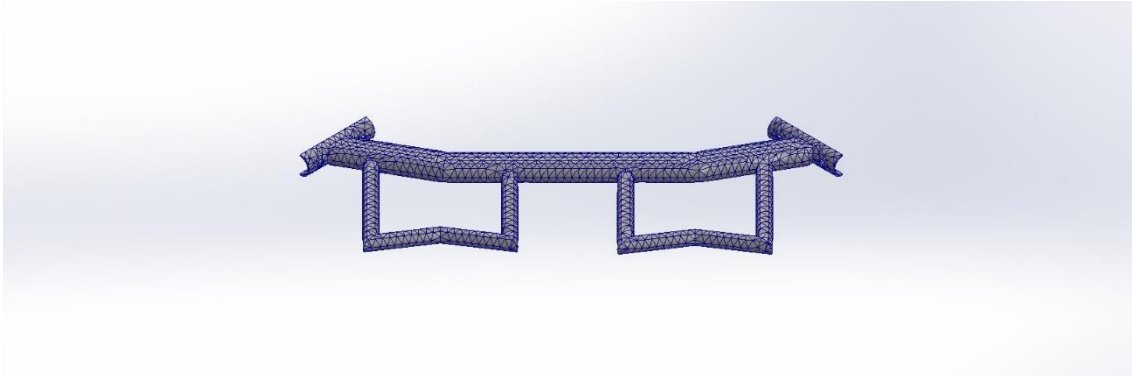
Análisis estático 4.5 Barra dominadas accesible. Fuente: Elaboración propia
